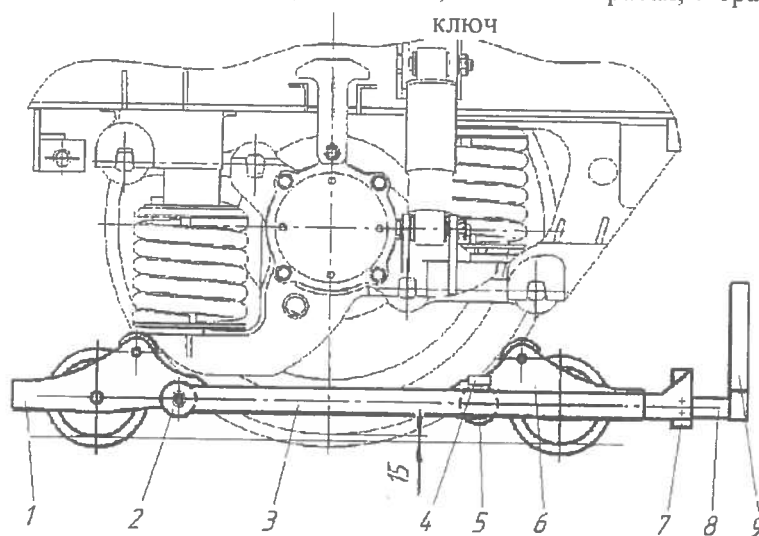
Приспособление для транспортировки тепловоза при заклинивании колесной пары
